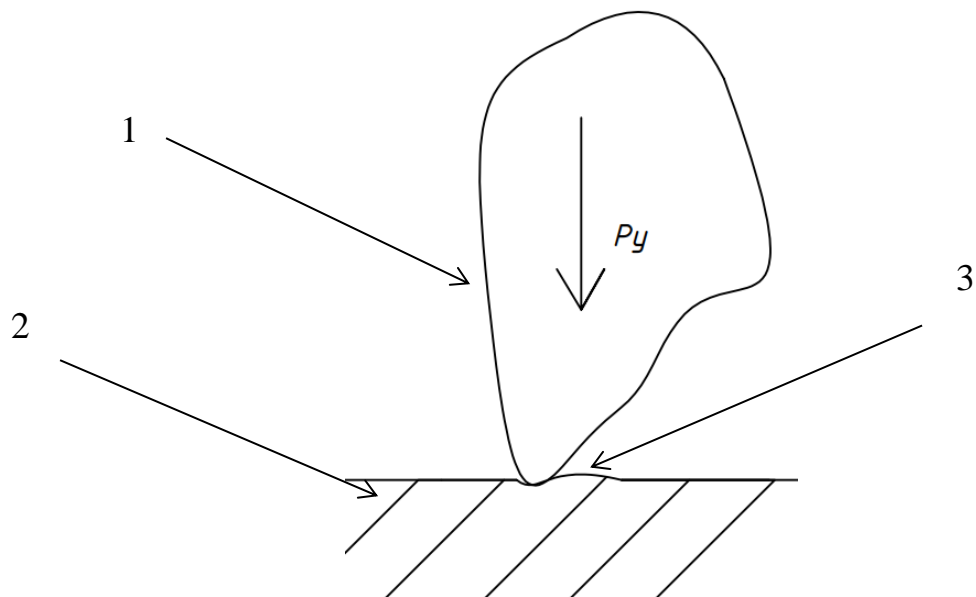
Взаємодія абразивного зерна з оброблюваною поверхнею: - 1. Абразивне зерно, 2. Заготовка, 3. Наплив
